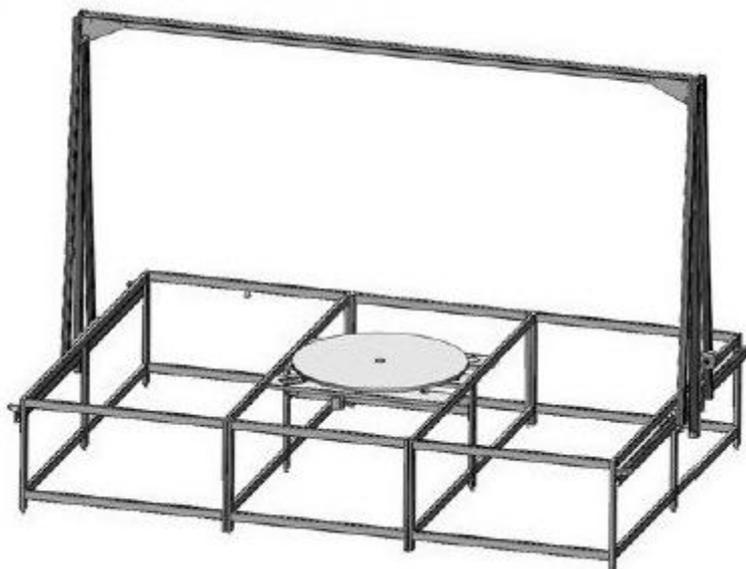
Пример общего вида станка с ЧПУ для фигурной резки пенопласта
